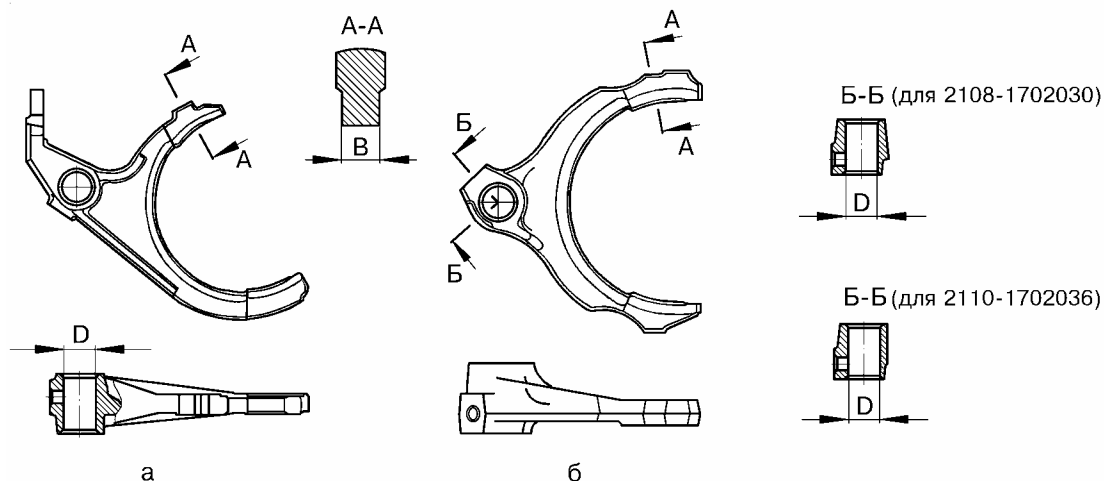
Вилка переключения передач: а - 2108-1702024; б - 2108-1702030, 2110-1702036.
